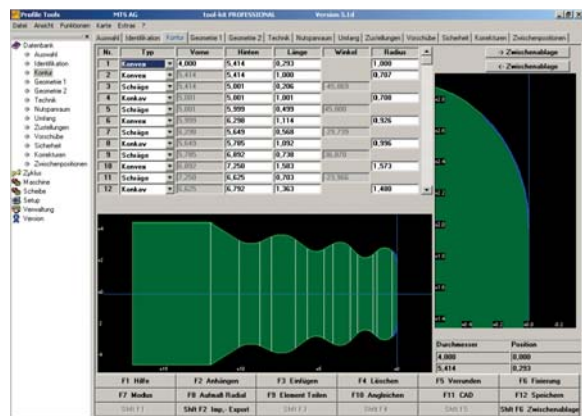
Konstruktion der Werkzeuggeometrie in *tool-kit
